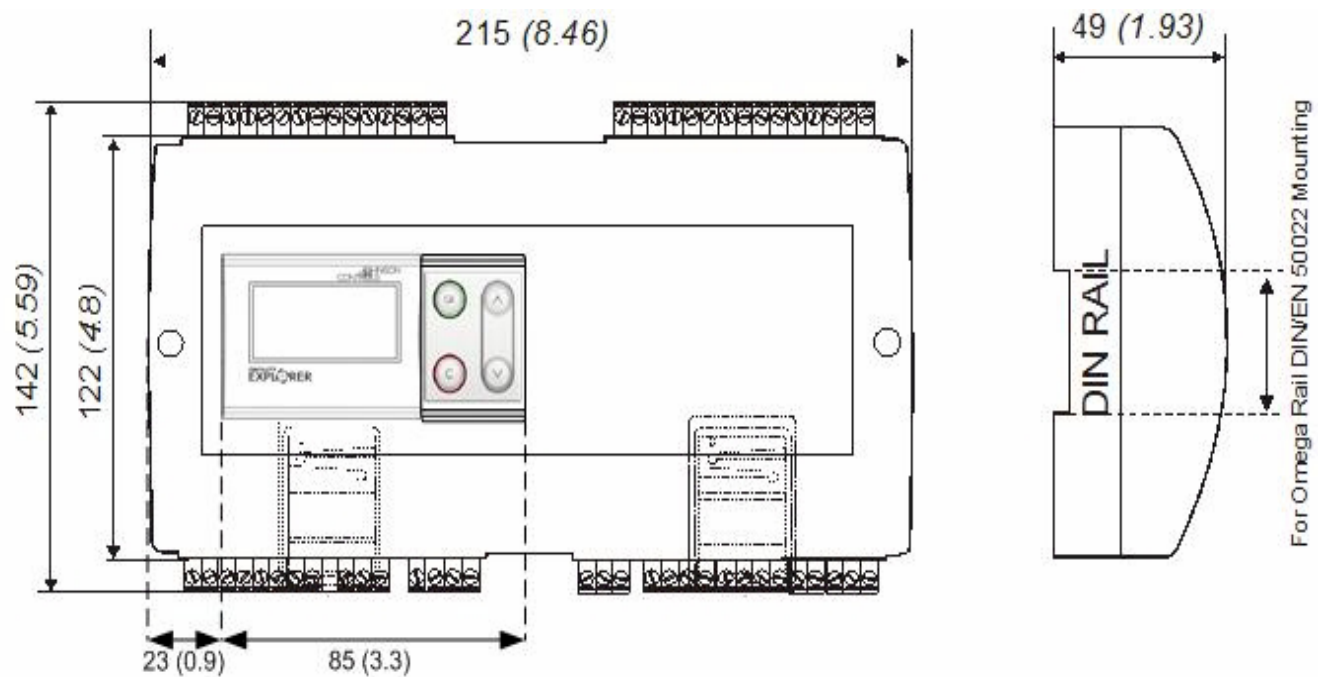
Dimensions du régulateur FX14 en mm (in.)
